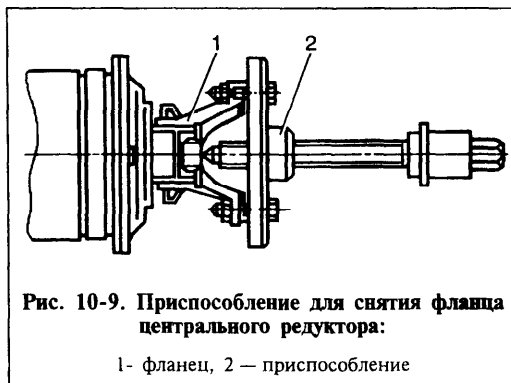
Приспособление для снятия фланца центрального редуктора:
